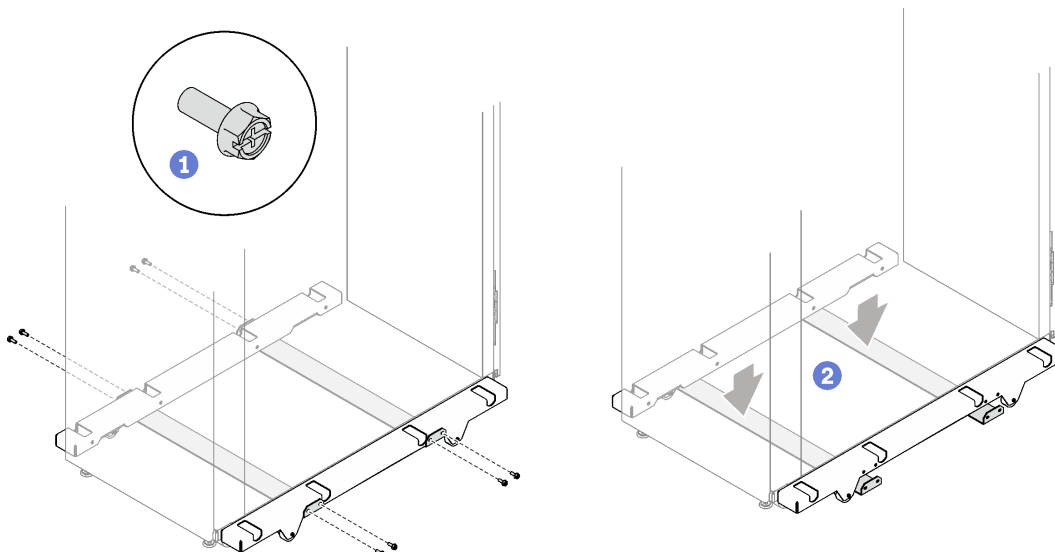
Rimozione delle barre stabilizzatrici degli stabilizzatori
